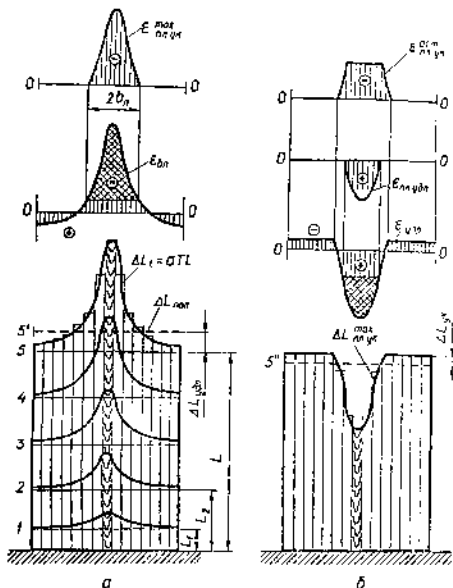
Механизм образования деформаций и напряжений при сварке
